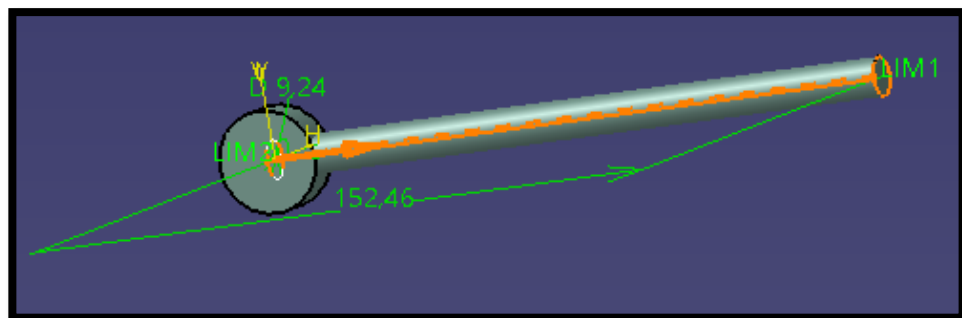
Seat mounting frame 11: Union trim brazo oscilante superior
